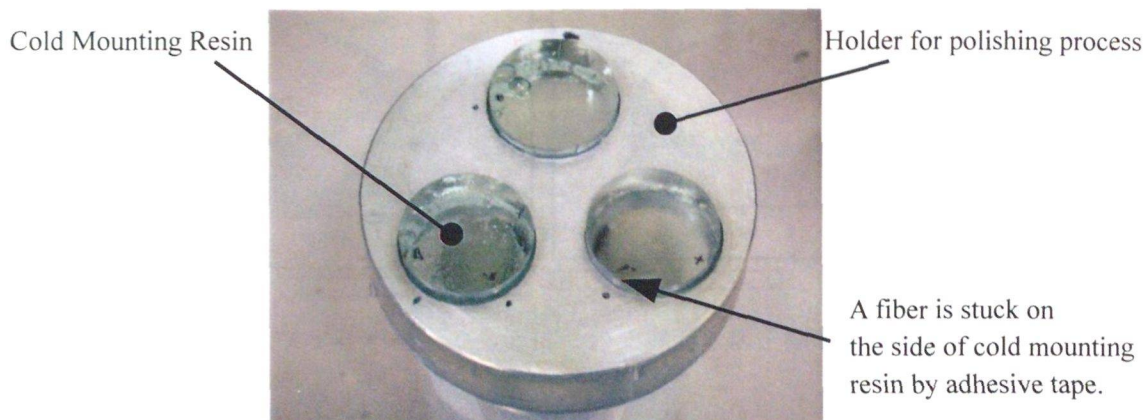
研磨加工用ホルダ治具とファイバの固定方法
